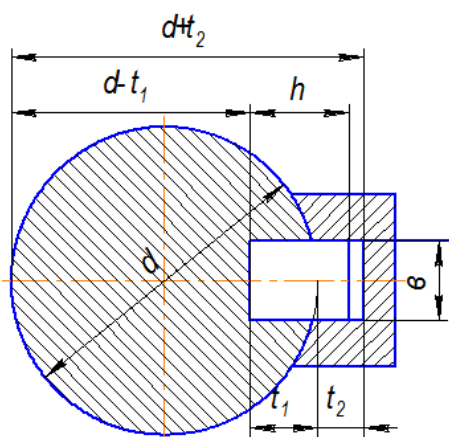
Основные размеры соединения с призматической шпонкой:
